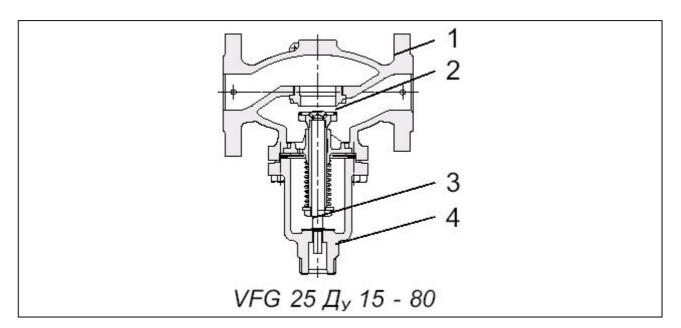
Устройство клапана VFG 25.* 1 – корпус клапана; 2 – седло клапана; 3 – золотник; 4 – крышка.
